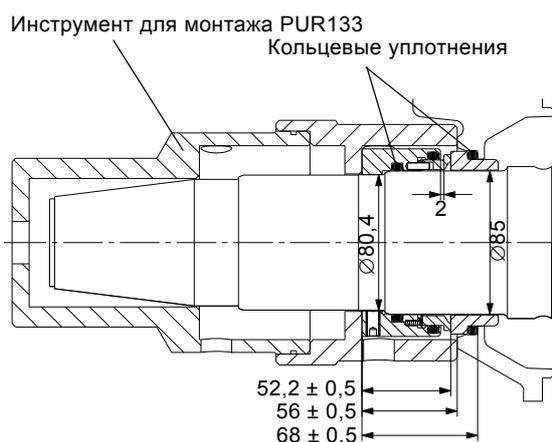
Установка вторичного уплотнения вала, типоразмер 72
